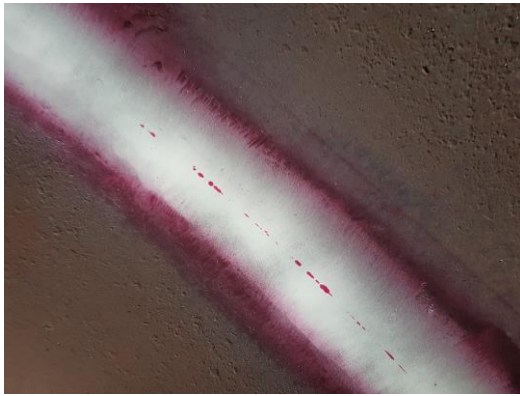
Дефект сварного шва на камере СОД
